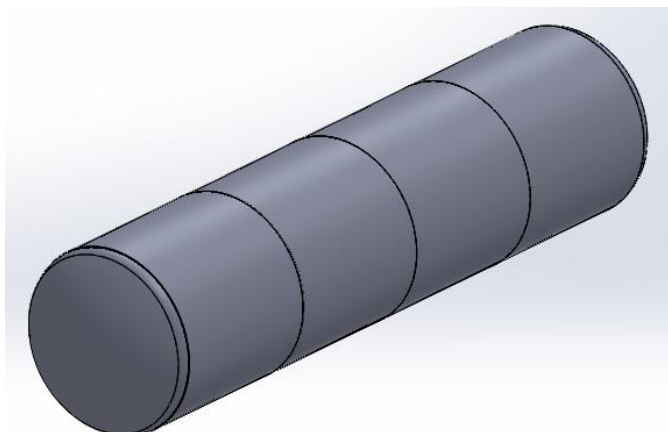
Ensamblaje de la cisterna completa sin accesorios vista por su fondo delantero
